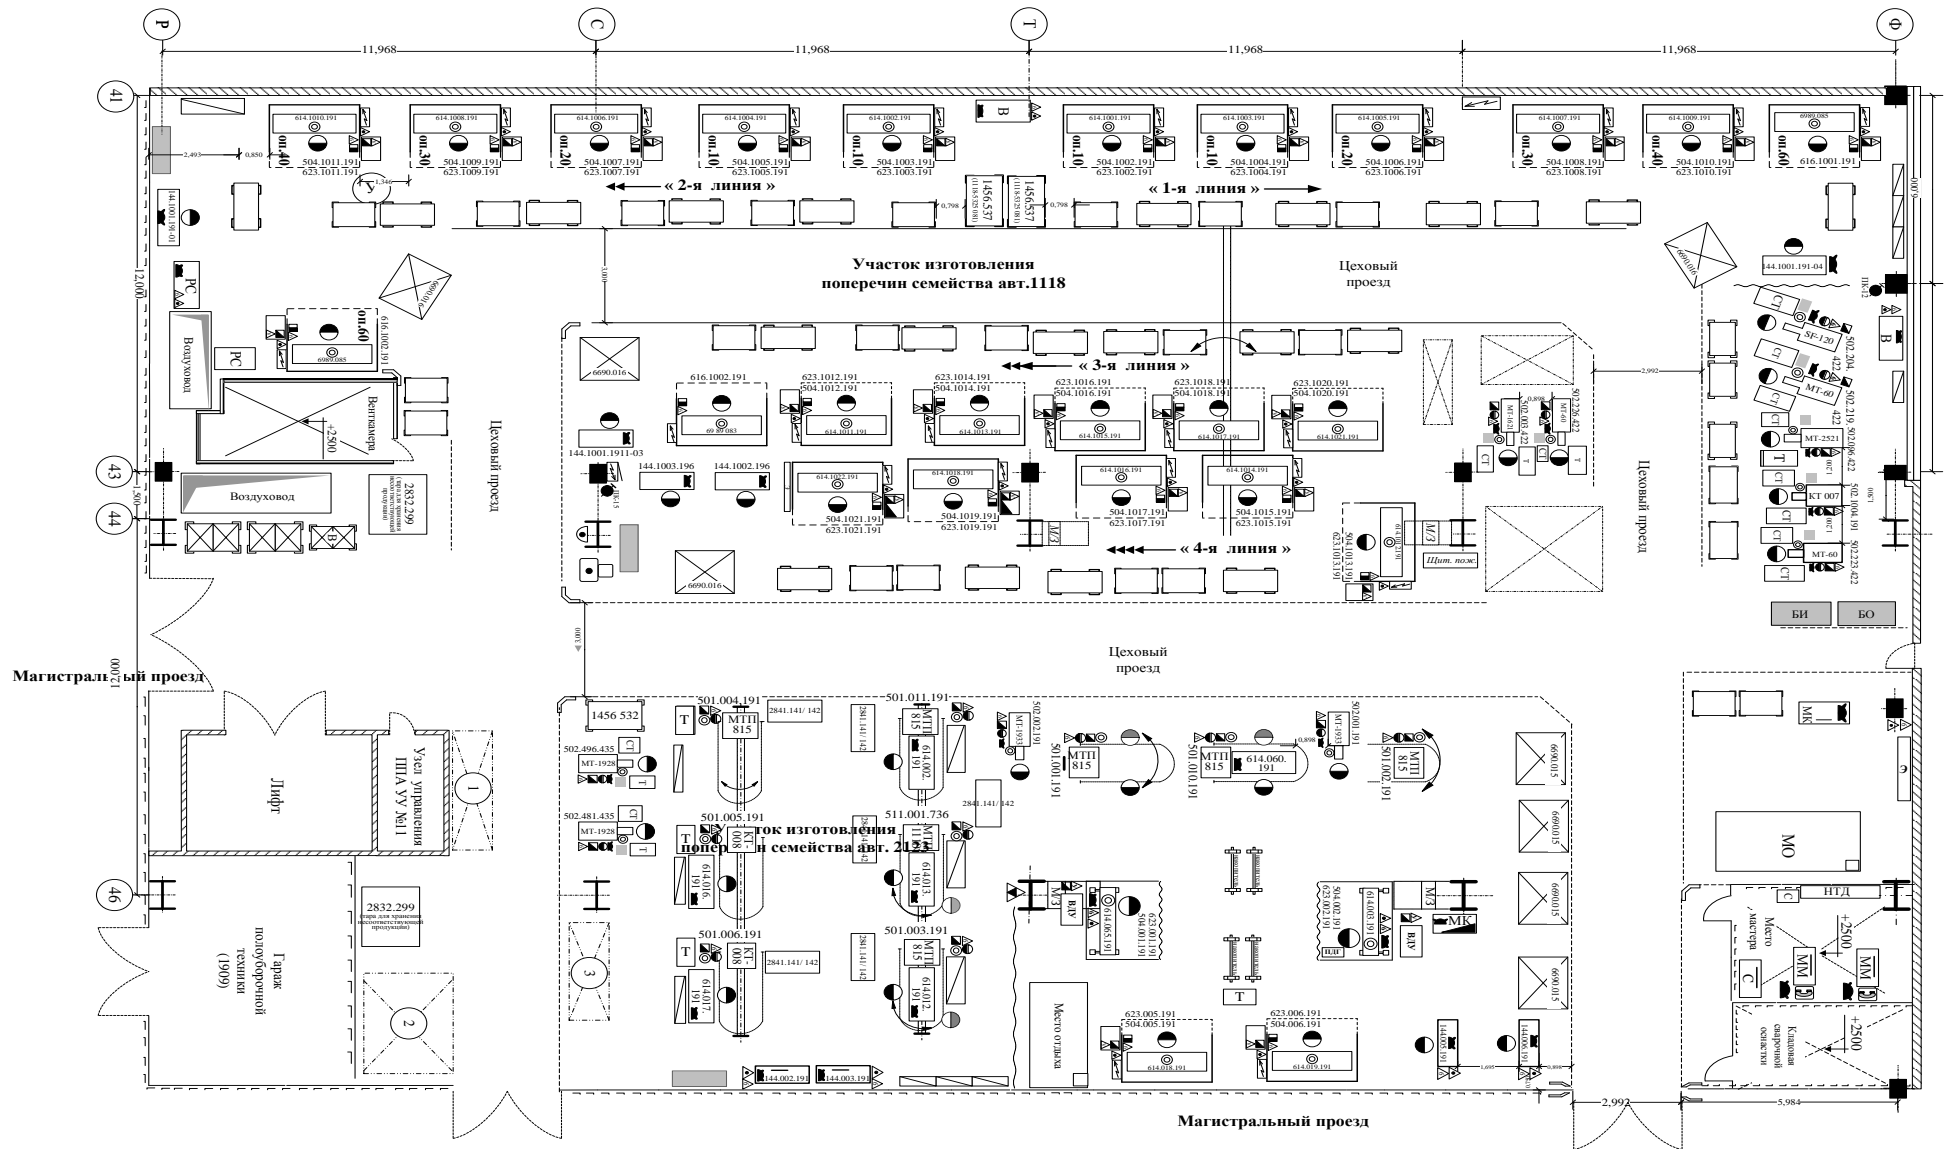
План размещения основного технологического оборудования сварочно-штамповочного цеха
